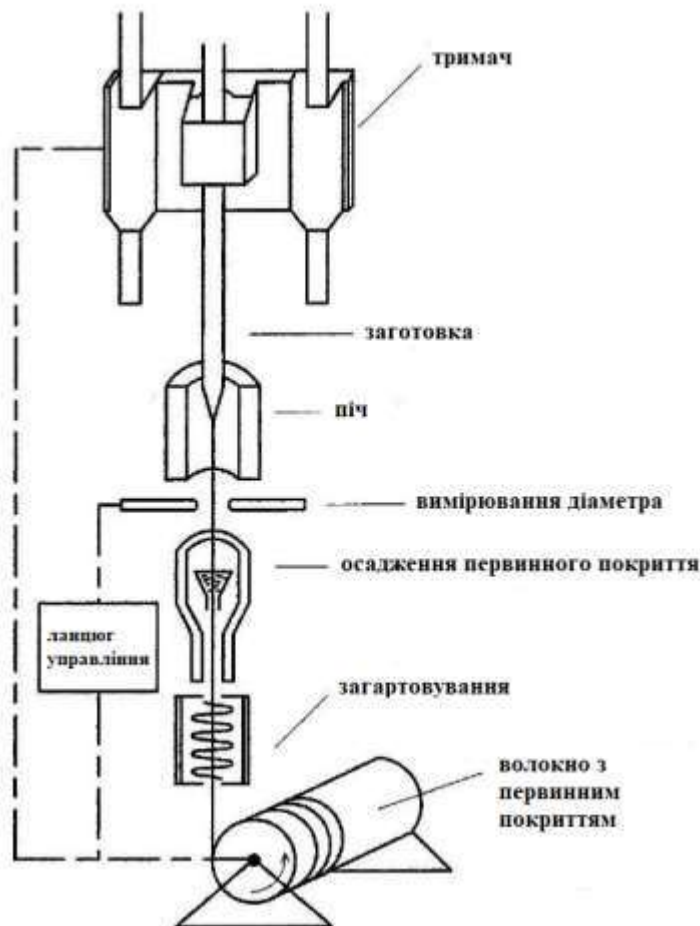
Витяжка із заготовки оптичного волокна
